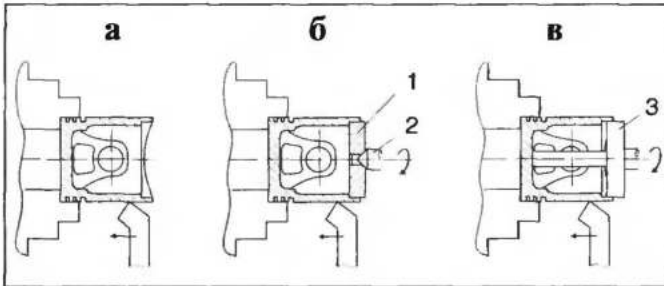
Возможные схемы установки поршня в токарном станке при обработке юбки:
